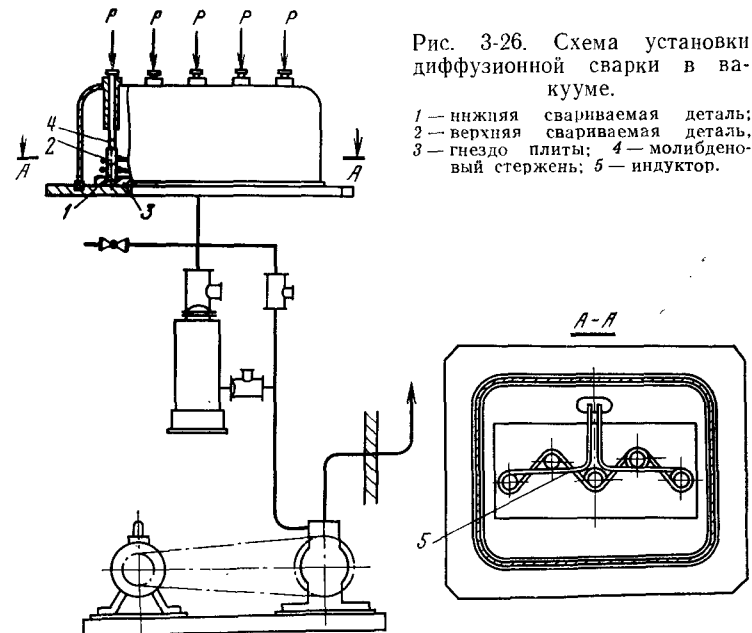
Схема установки диффузионной сварки в вакууме.
